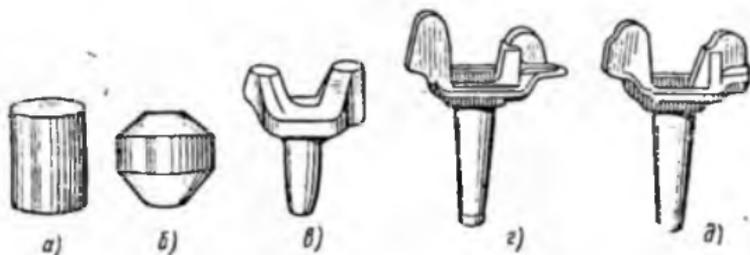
Переходы при изготовлении поворотного кулачка горячим комбинированным выдавливанием:
